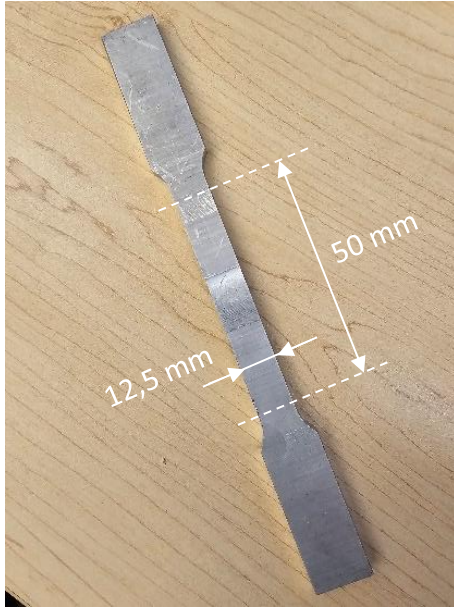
Éprouvette de soudure pour les essais de traction
